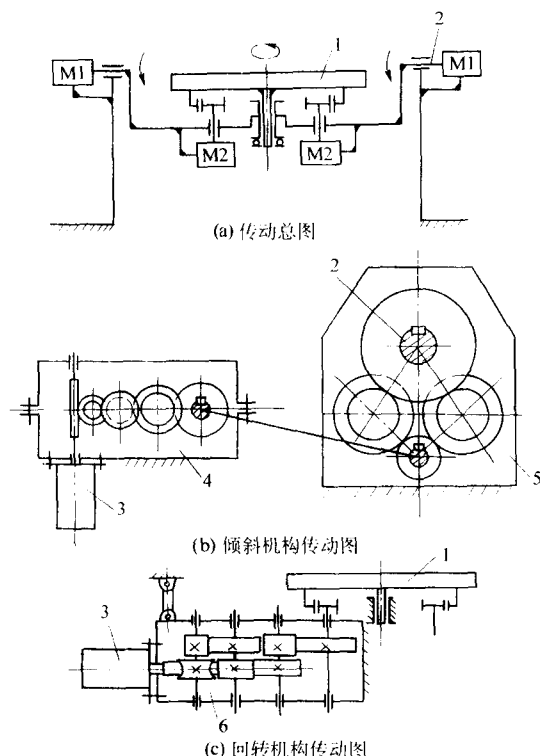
100 t 双座式数控焊接变位机传动简图
